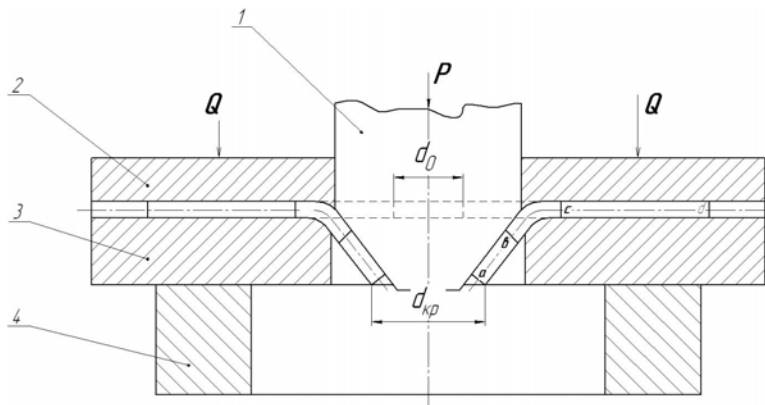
Общий вид штампа: 1 – пуансон; 2 – прижим; 3 – матрица; 4 – подкладное кольцо
